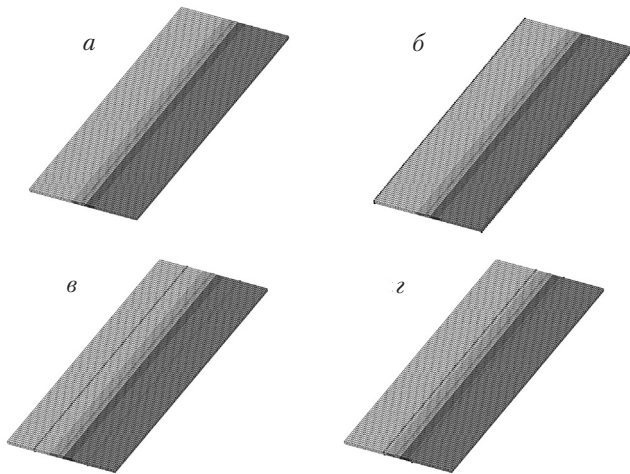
3D-модель сварного соединения с вариантами закрепления: а – без закрепления; б – закрепление на базе 200 мм; в – закрепление на базе 100 мм; г – закрепление на базе 50 мм.
